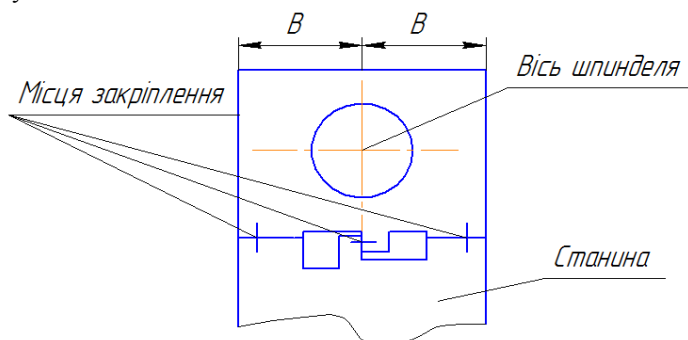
Симетрична конструкція корпусу шпиндельної бабки
